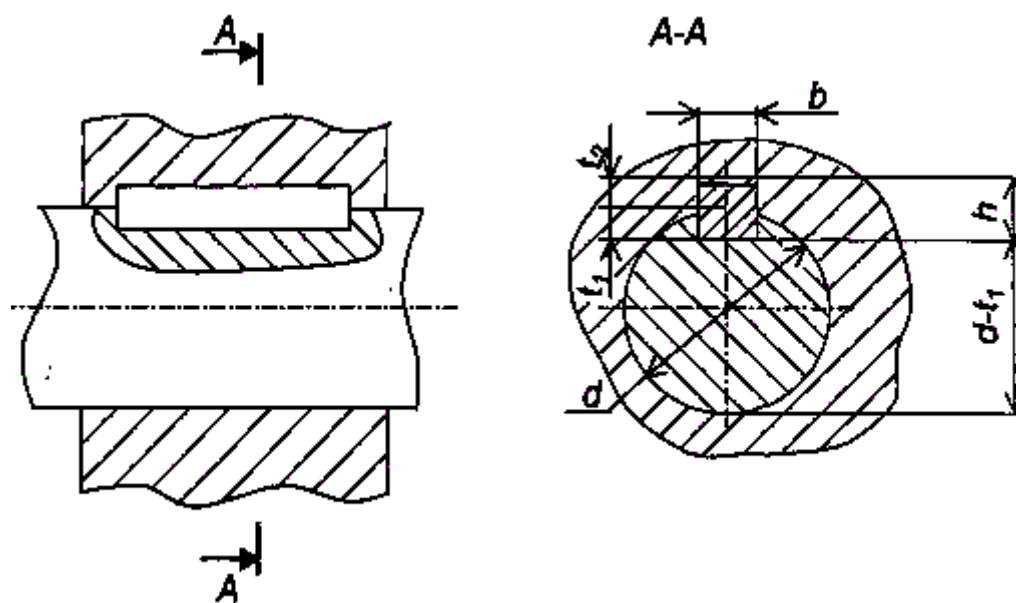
Схема шпоночного соединения вала с рабочим колесом
